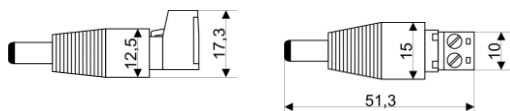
Vista meccanica e dimensioni dell'alimentatore.
